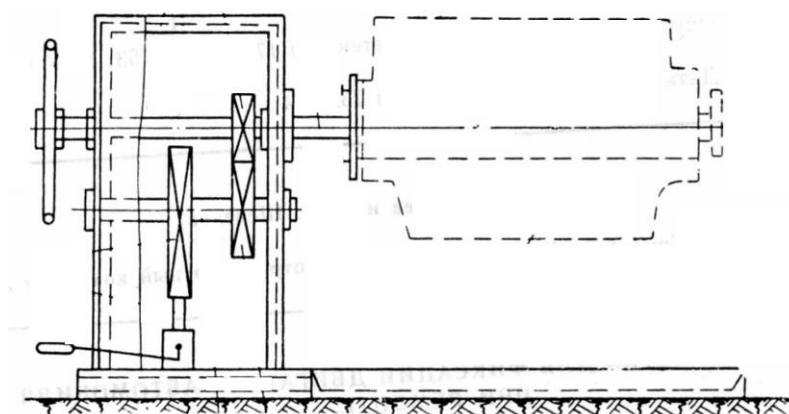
Приспособление для крепежа КП и агрегатов при обслуживании
